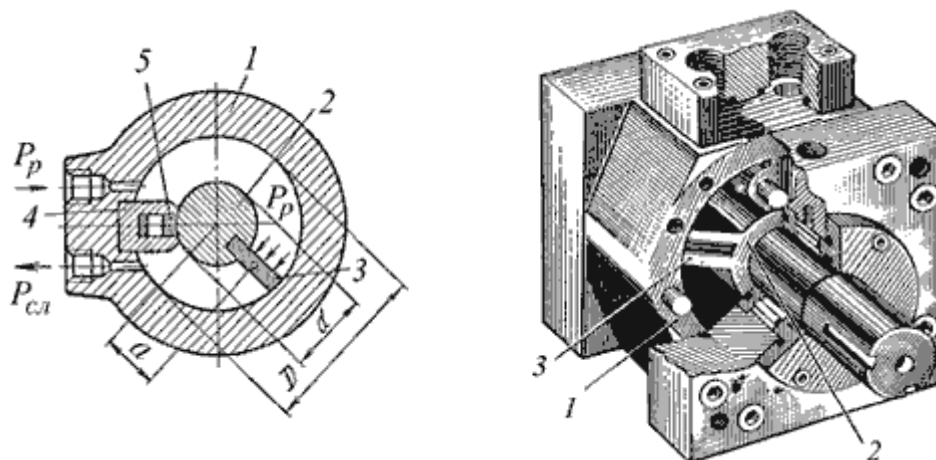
Поворотный однолопастной гидроцилиндр:
